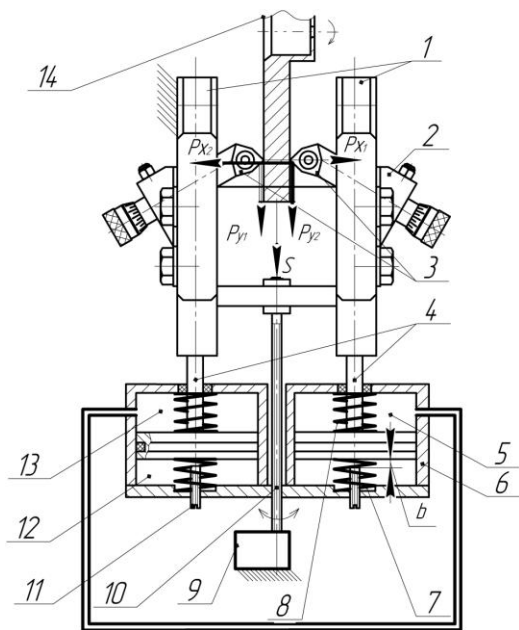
Установка для обработки рабочих поверхностей тормозного диска:
